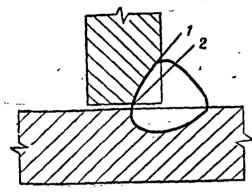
а. Схема расчетных сечений сварного соединения с угловым швом 1 -- сечение по металлу шва, 2— сечение по металлу границы металлу ллу границы сплавления
